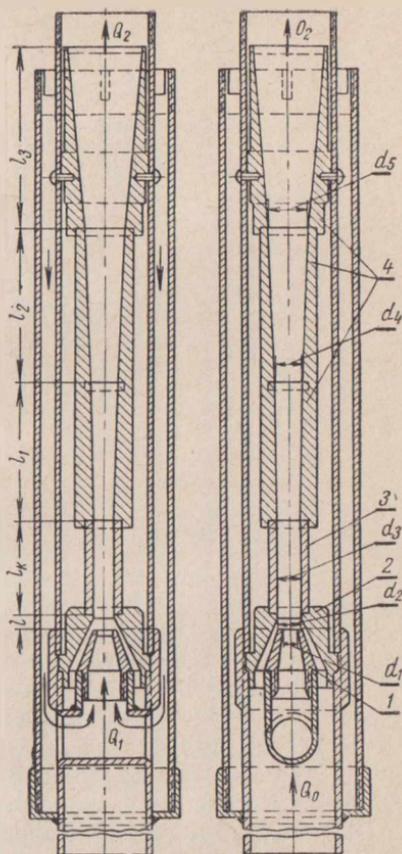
Струйный аппарат сварной конструкции:
